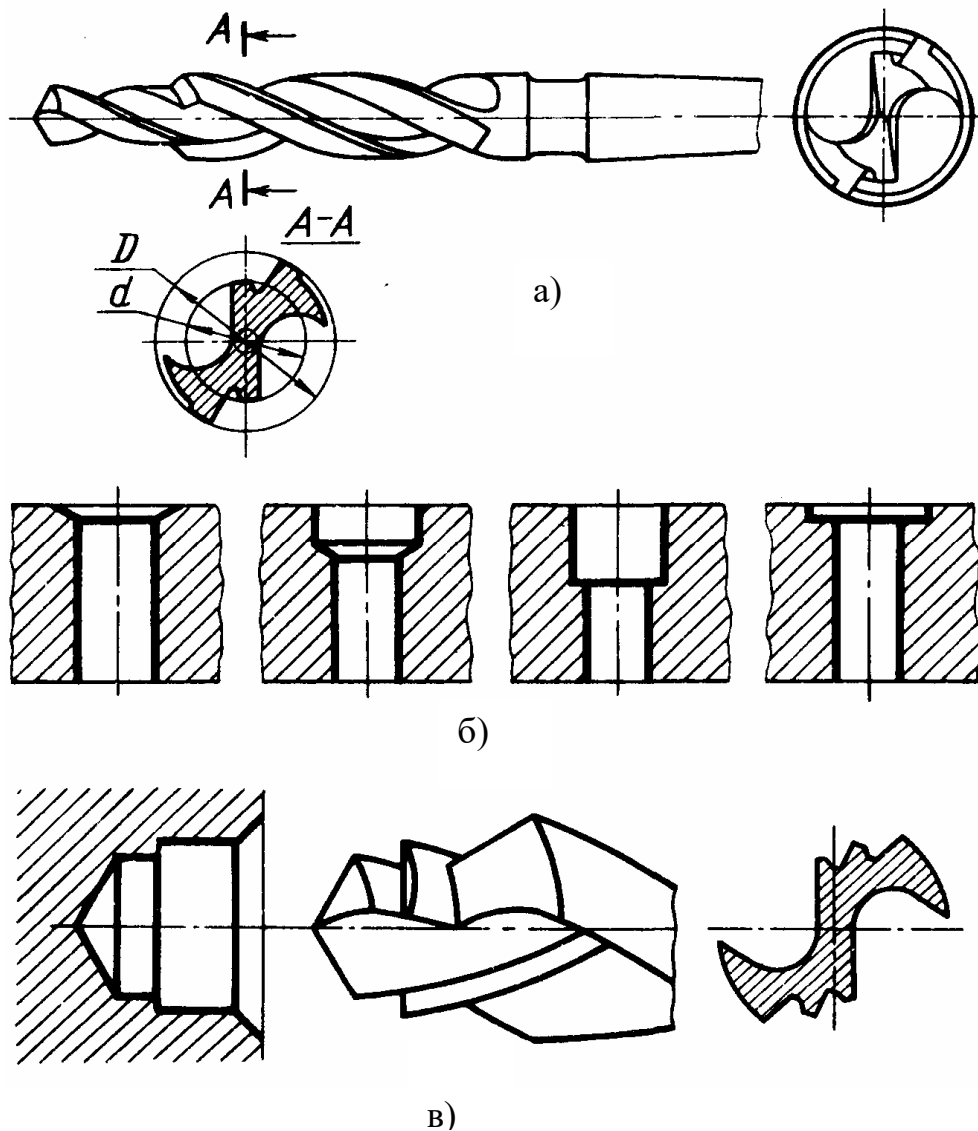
Схеми обробки отворів комбінованими свердлами: а – чотиристрічкове свердло; б – елементи деталей оброблені з використанням чотиристрічкових свердел; в – обробка отвору шестистрічковим свердлом
